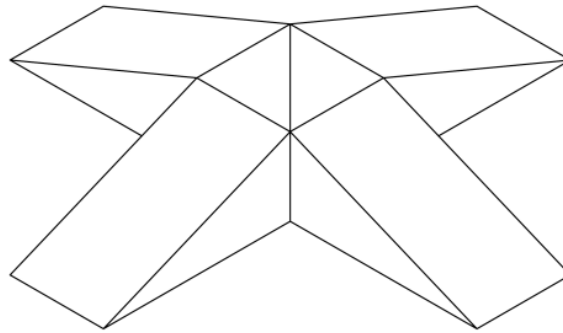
20: Vista isométrica del ensamble de la salida. Fuente: Elaboración propia.
